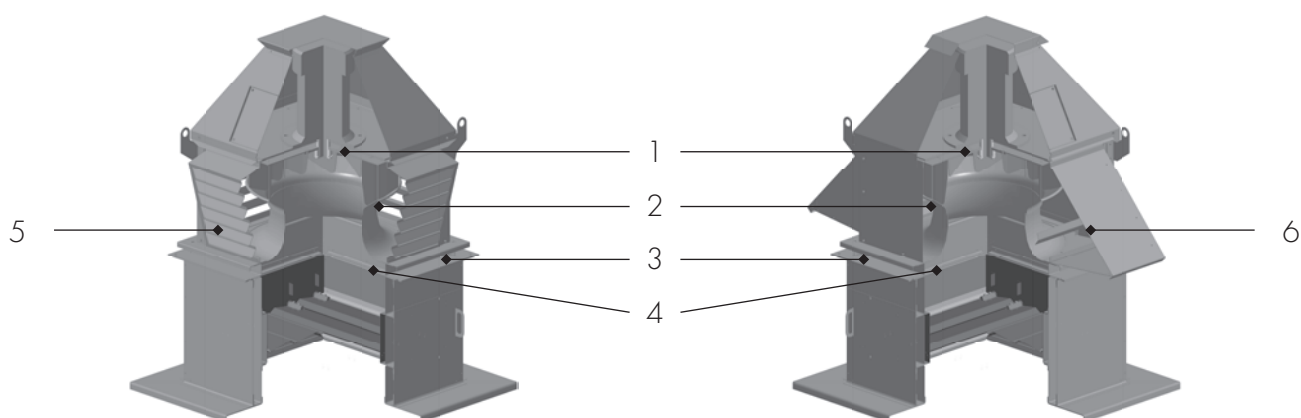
Устройство и основные элементы вентиляторов крышных радиальных. Корпус изготавливается из оцинкованной стали (для некоторых исполнений — из нержавеющей стали).
